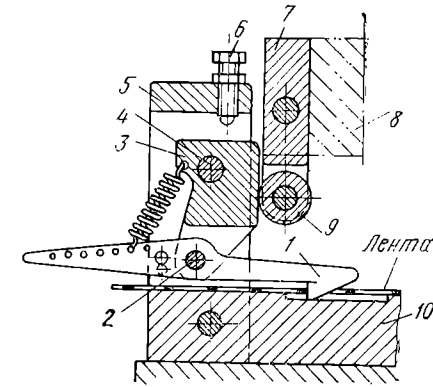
Крючковое устройство для подачи ленты или полосы в штамп
